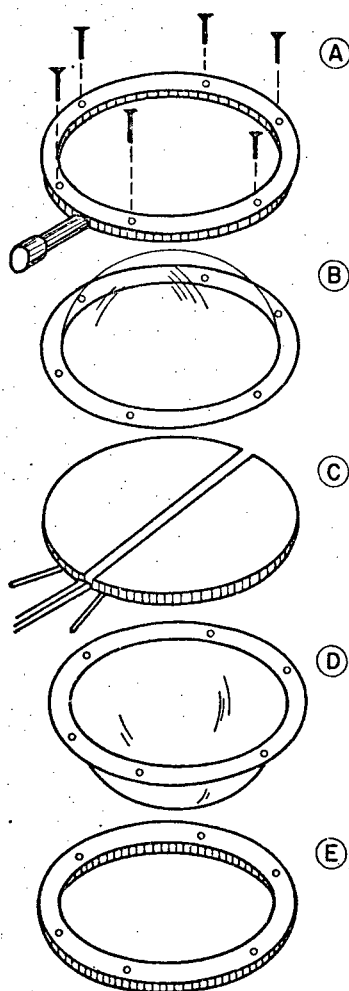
Vista explodida do instrumento de Fritschen [12],[18].
